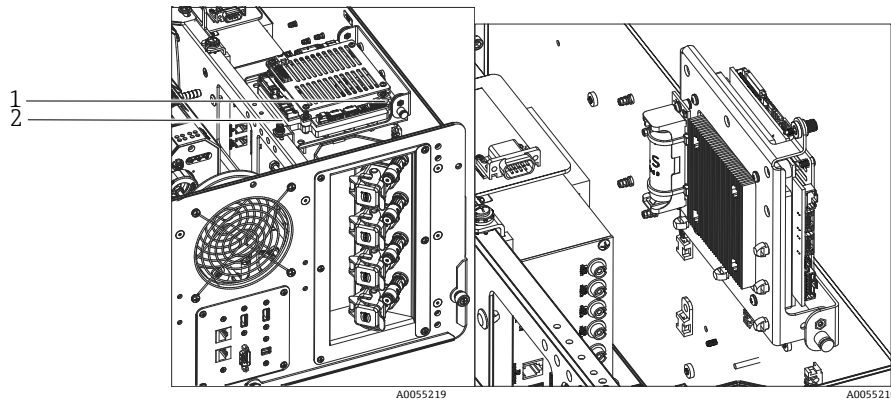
Vue d'ensemble arrière avec plaque de contrôleur en position ouverte
